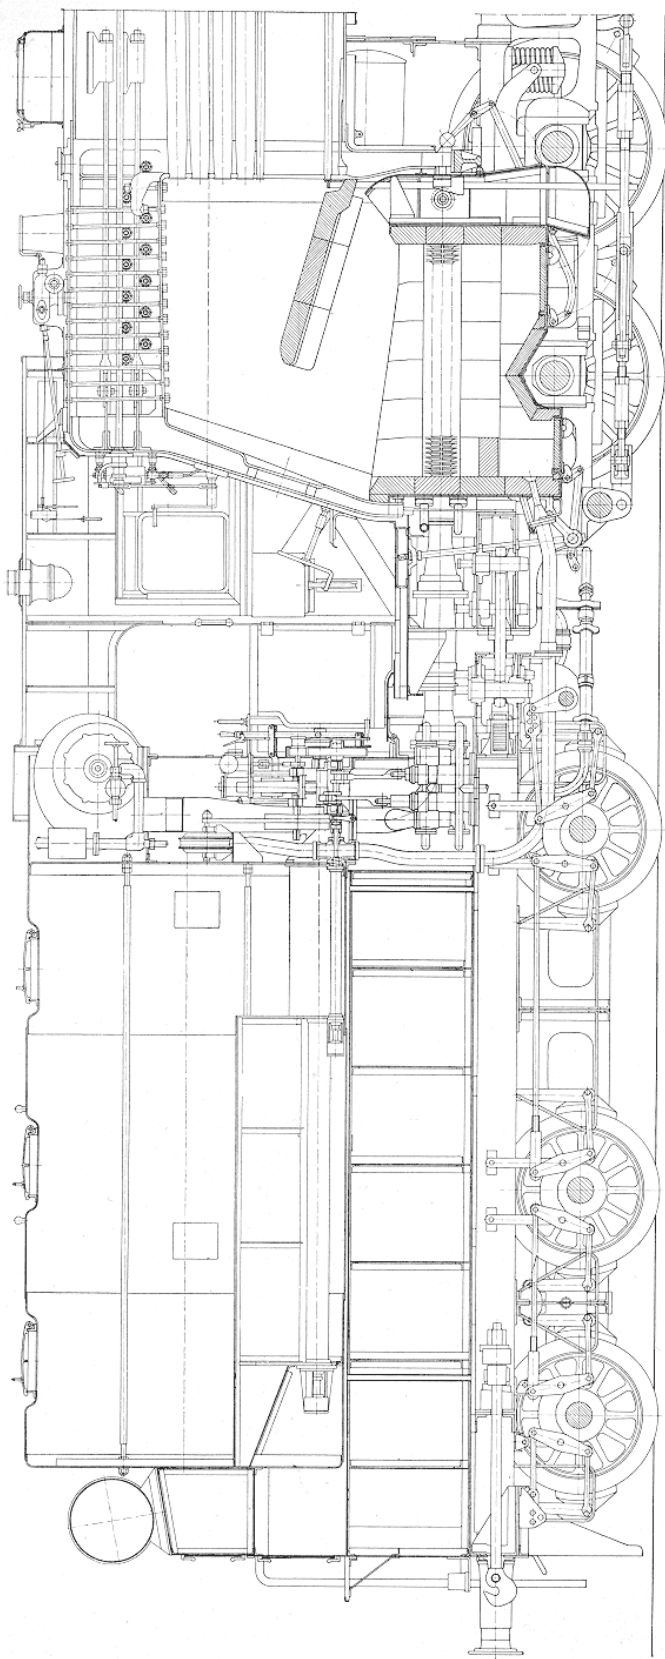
Kohlenstaub-Lokomotive, Längsschnitt und Grundriß.
